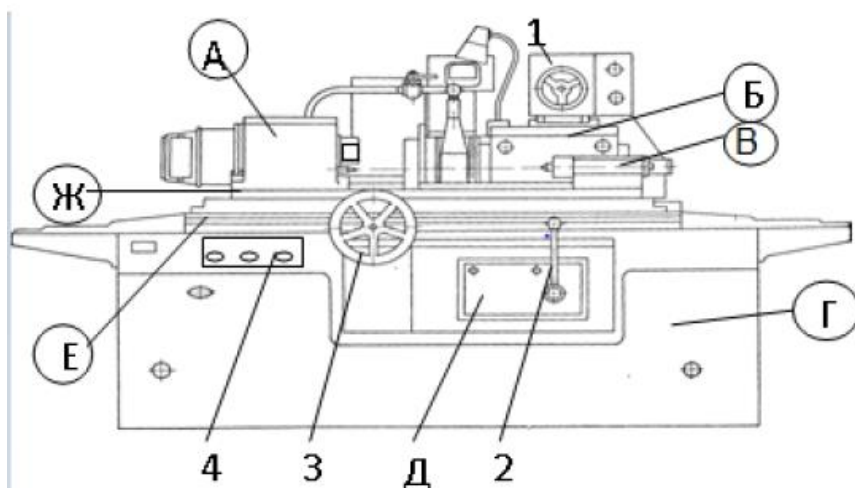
Общий вид кругло-шлифовального станка модели 3151
